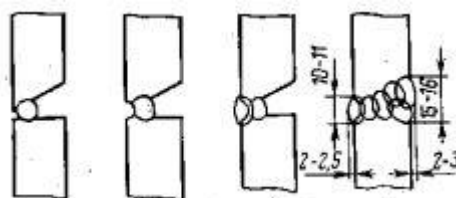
Последовательность наложения слоев полуавтоматической сварки в углекислом газе, где сварка проходит при заполнении разделки горизонтального шва.
